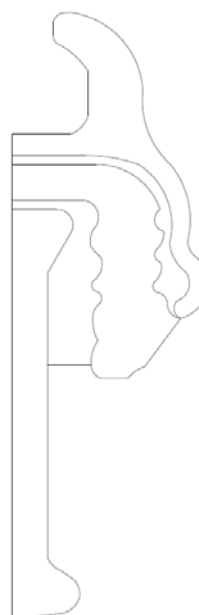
Desenho CAD de um *stub* (U160BS)
